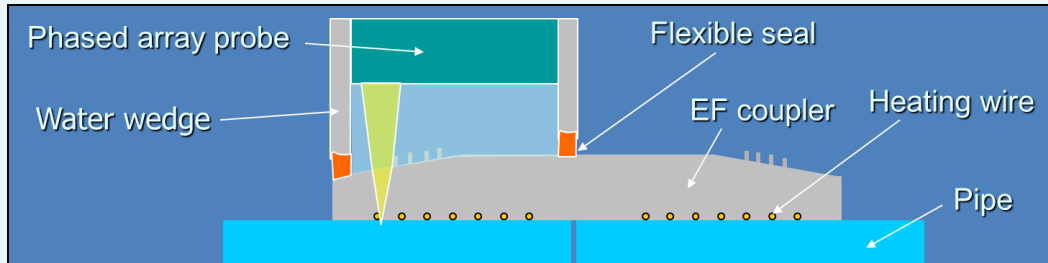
Esquema de inspección de soldaduras por electrofusión
